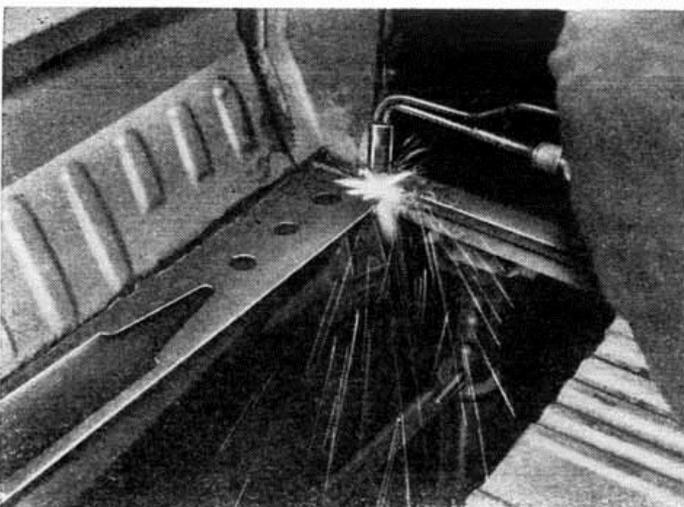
Trennen der Schweißverbindung Ausleger mit der Seitenwand
